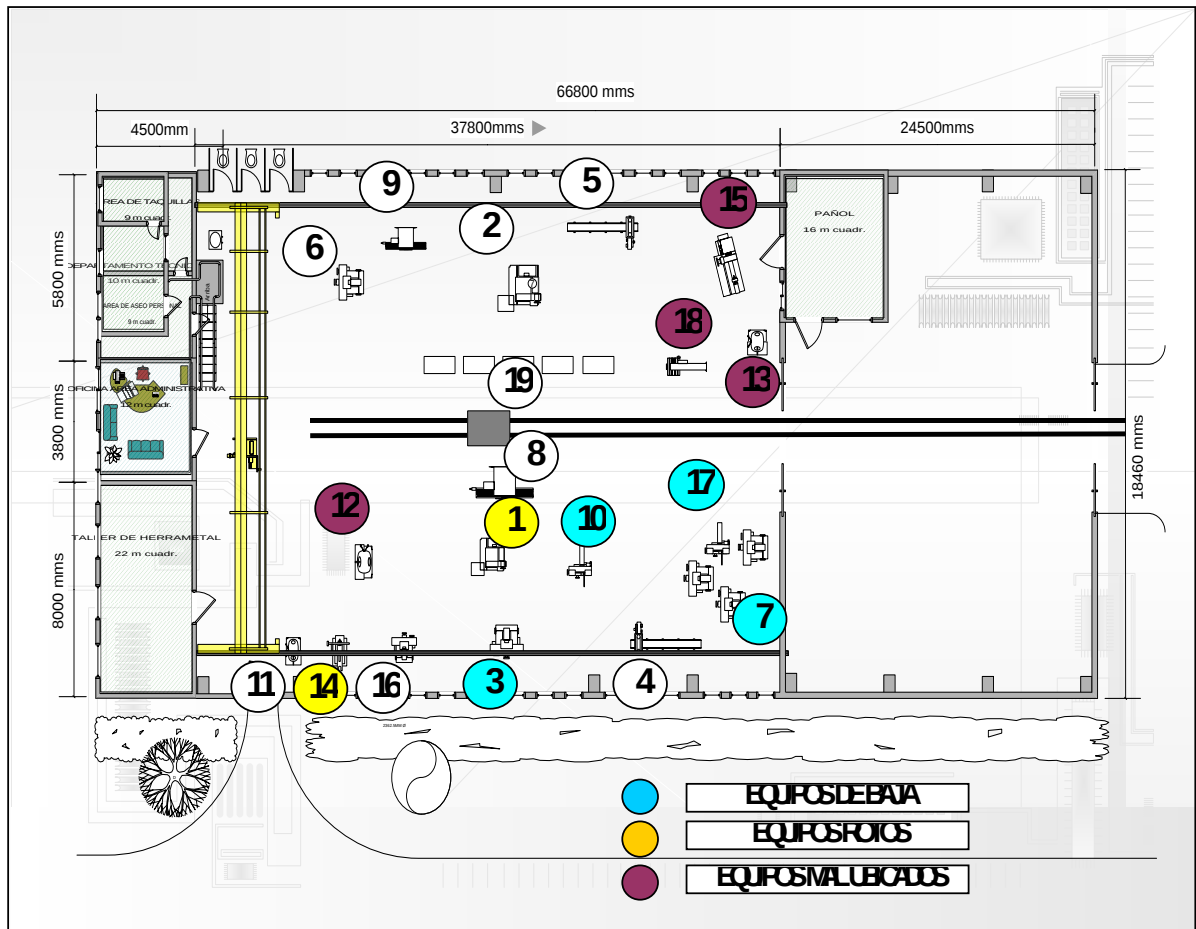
Distribución en planta actual. Fuente: Elaboración propia.
